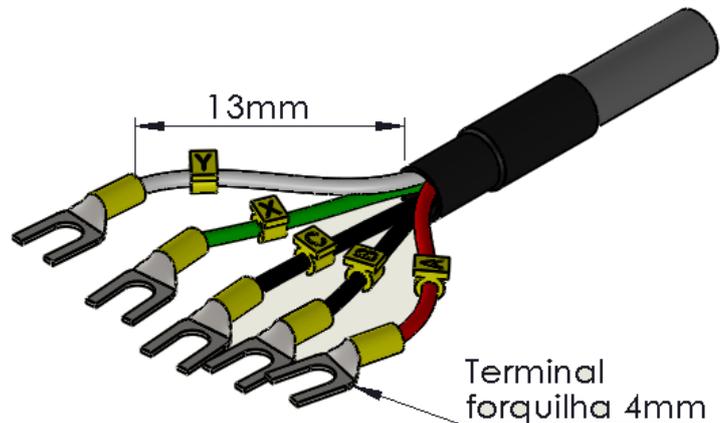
Cabo do sinal dos eletrodos e alimentação bobina
